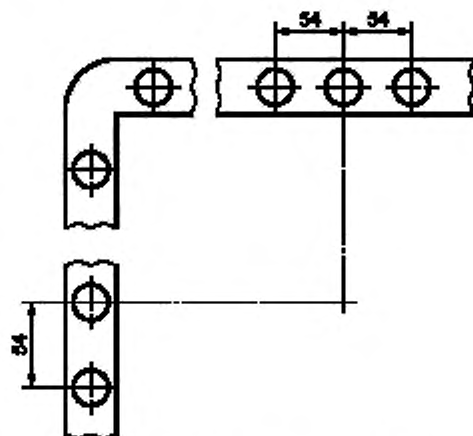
Присоединительные размеры прямоугольных фланцев с расположением нечетного количества отверстий по сторонам H и B
